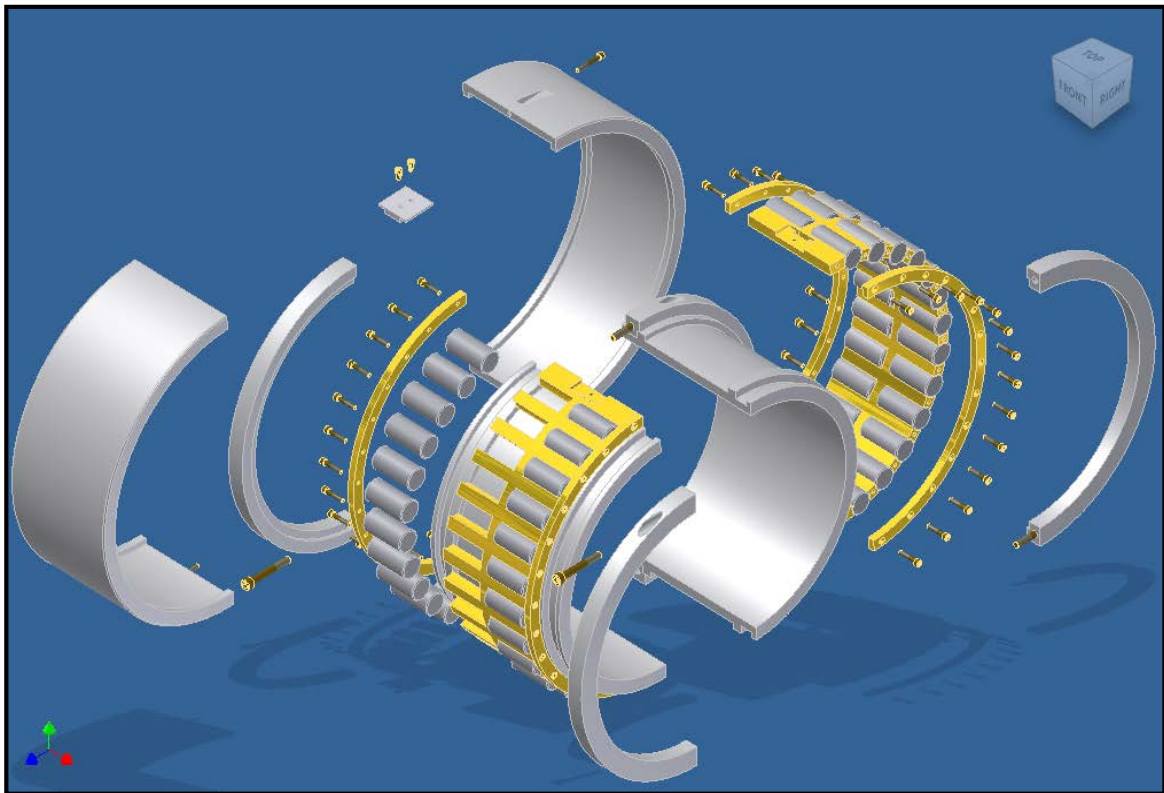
Rodamiento desarmable de dos hileras de rodillos
